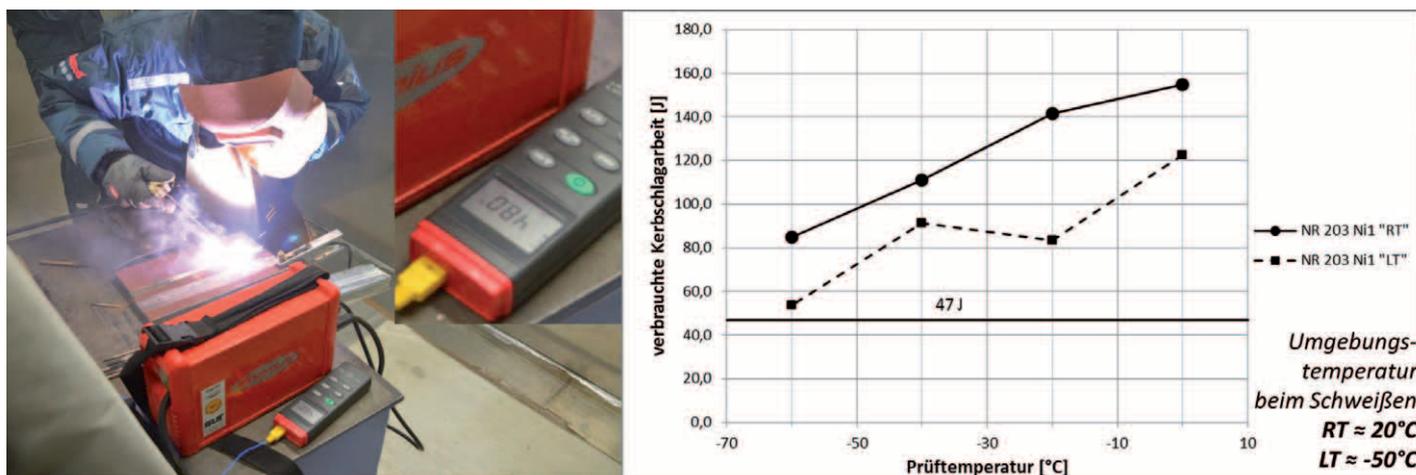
Reparatur-Schweißversuch bei -48°C (links); Bewertung der Kerbschlagarbeit für eine Innershield-Schweißnaht bei verschiedenen Umgebungsbedingungen (rechts).
